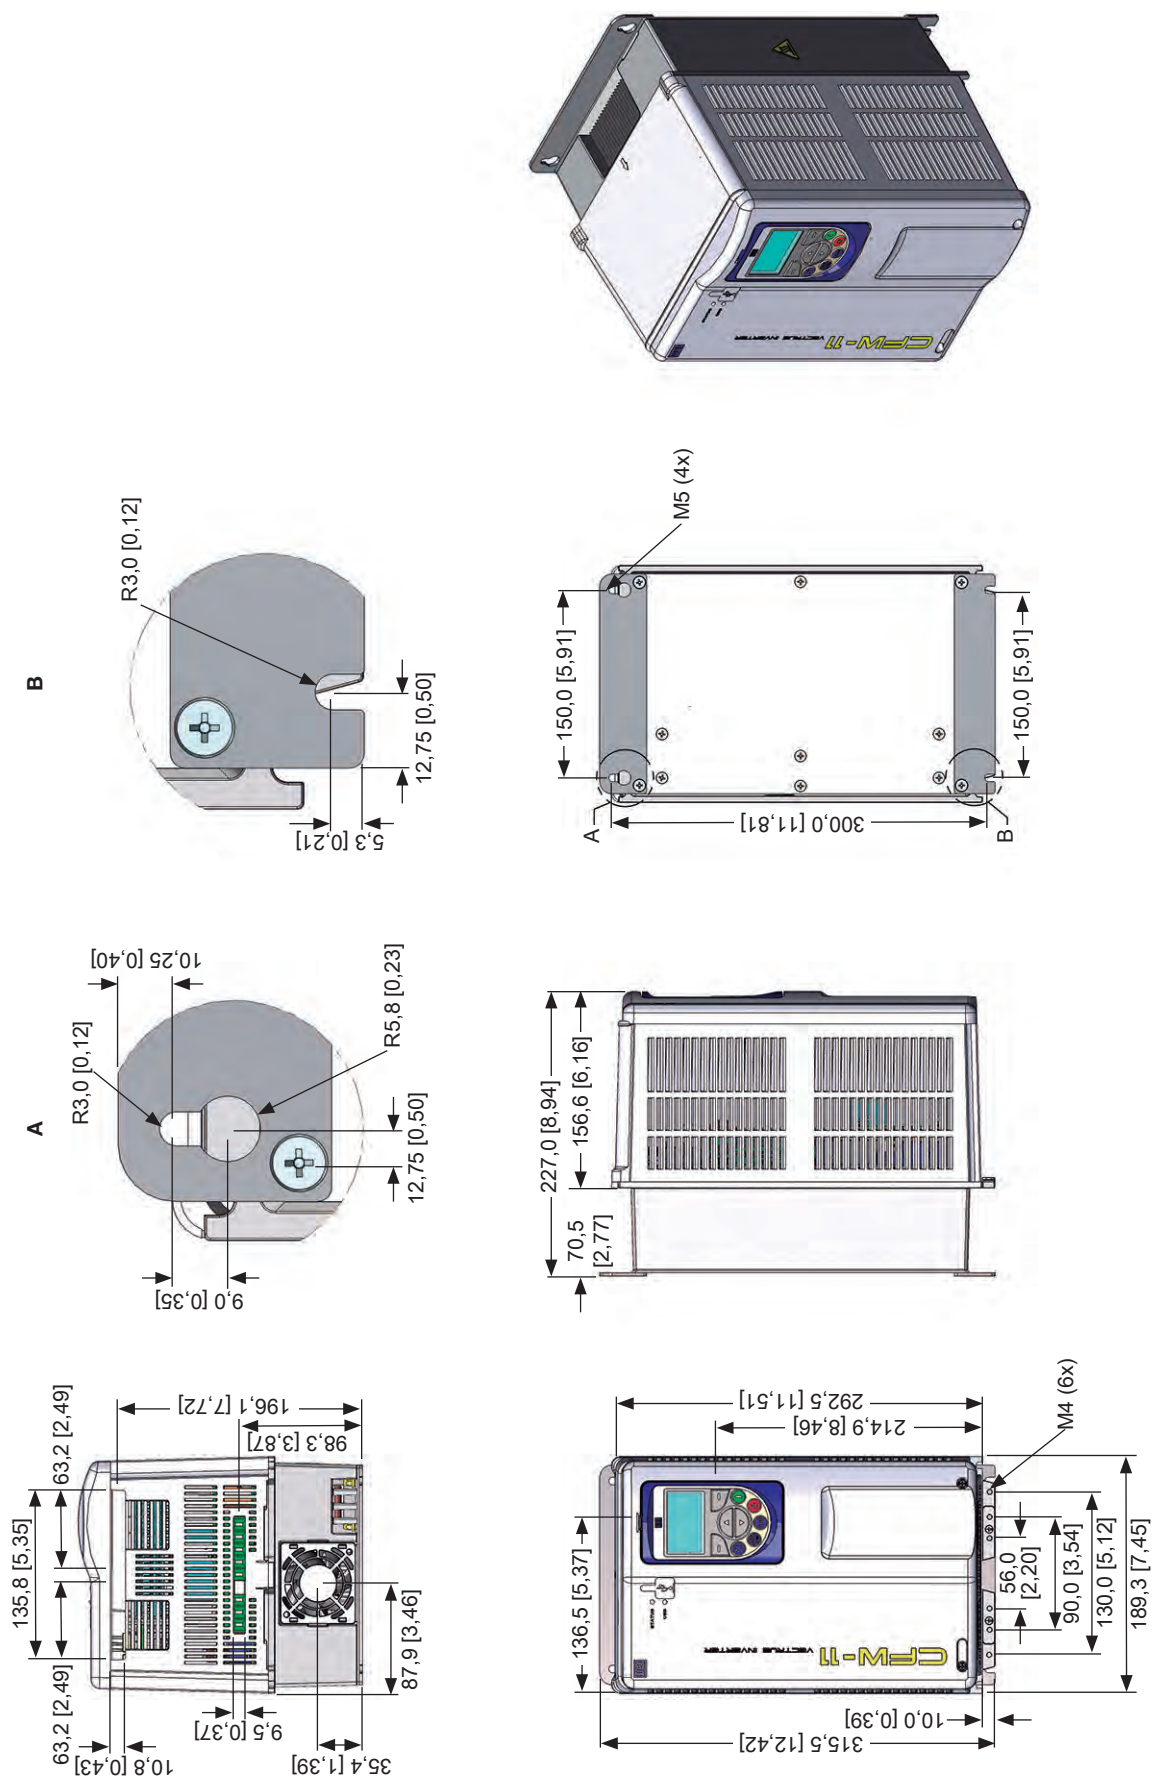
Габаритные размеры преобразователя, размер корпуса В, мм [дюйм.]
